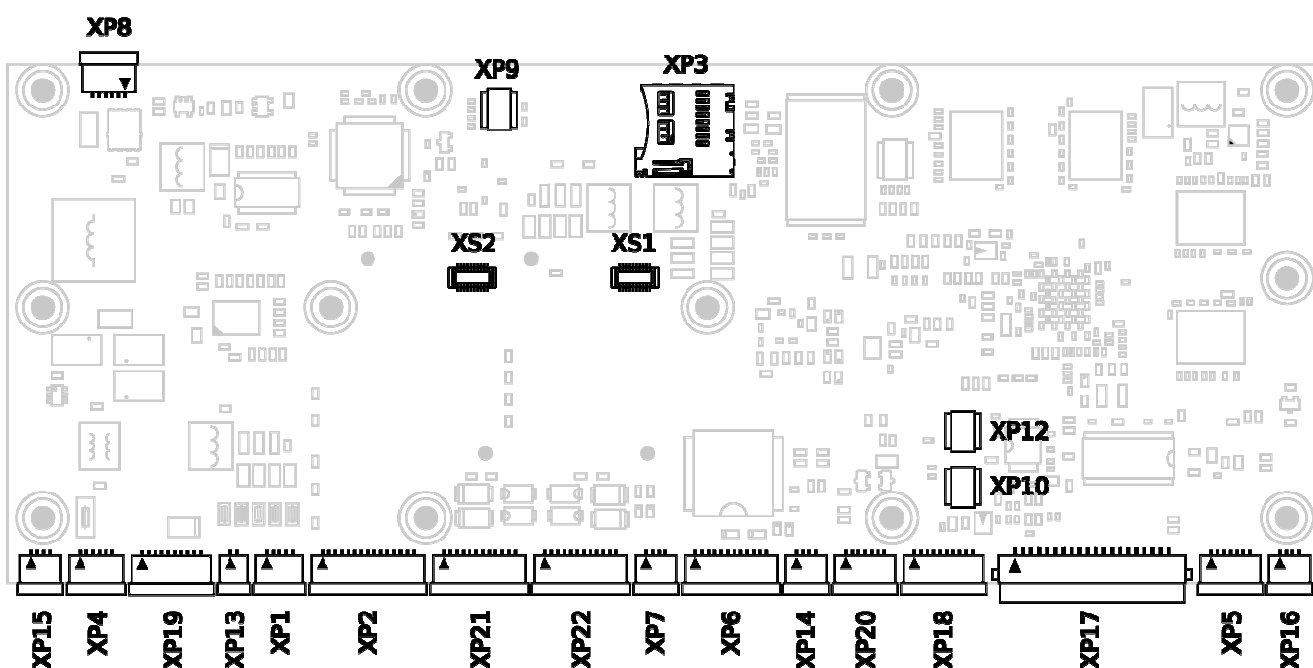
Внешний вид модуля «Вычислитель-ВМ14Я-П» – вид со стороны соединителей.
